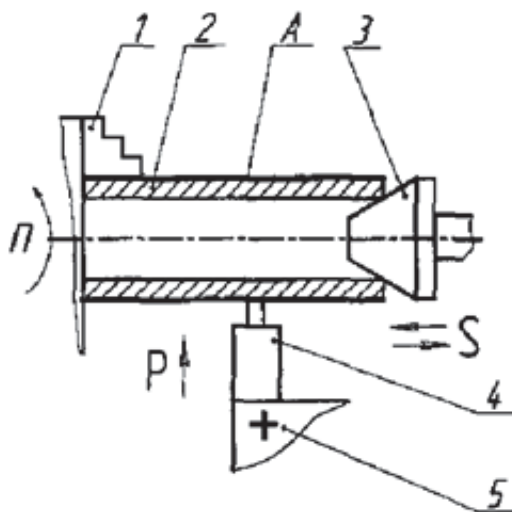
Схема нанесения защитного покрытия твердым инструментом: 1 – трехкулачковый патрон, 2 – обрабатываемая деталь, 3 – центр задней бабки, 4 – приспособление для ФАБО, 5 – резцедержатель токарного станка, А – обрабатываемая поверхность
